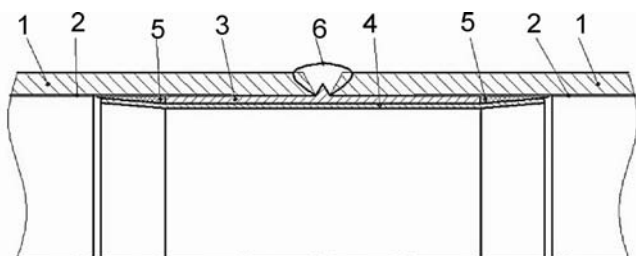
Сварное соединение труб с внутренним покрытием с применением втулки подкладной Aitech без использования герметизирующей мастики:
